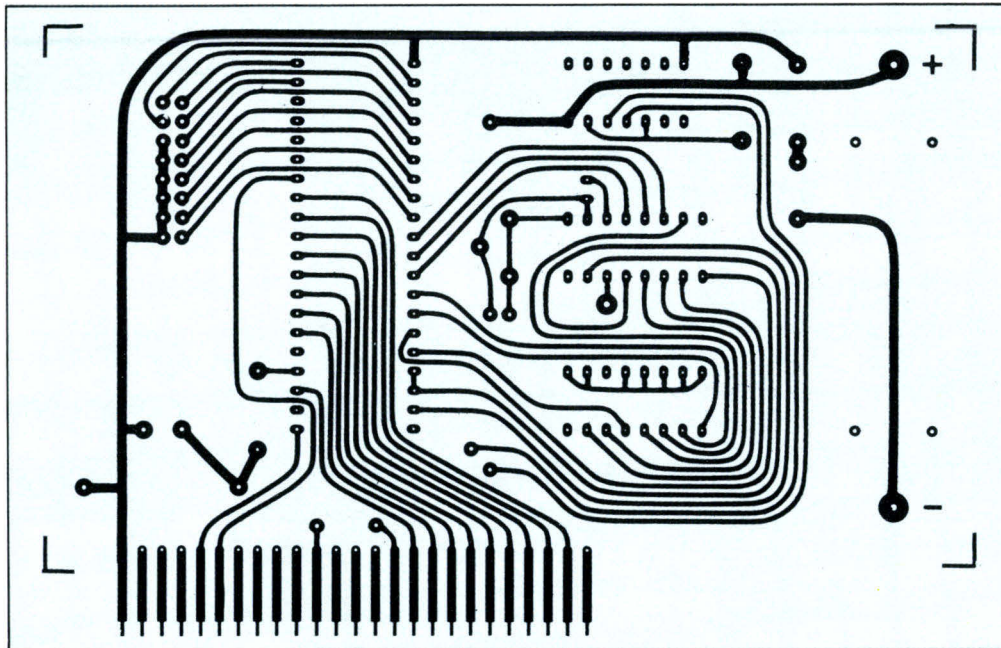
b. - Circuit imprimé vu côté soudures.
